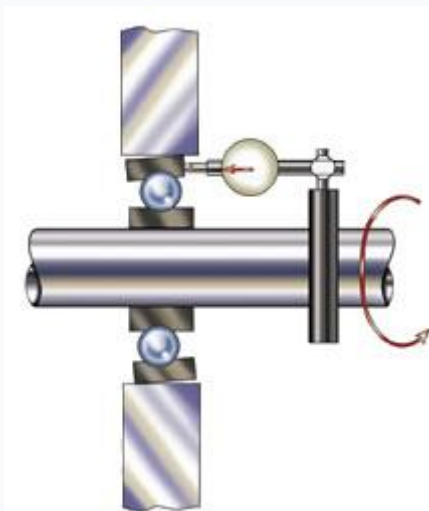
Измерения биения подшипника с помощью стрелочного индикатора
